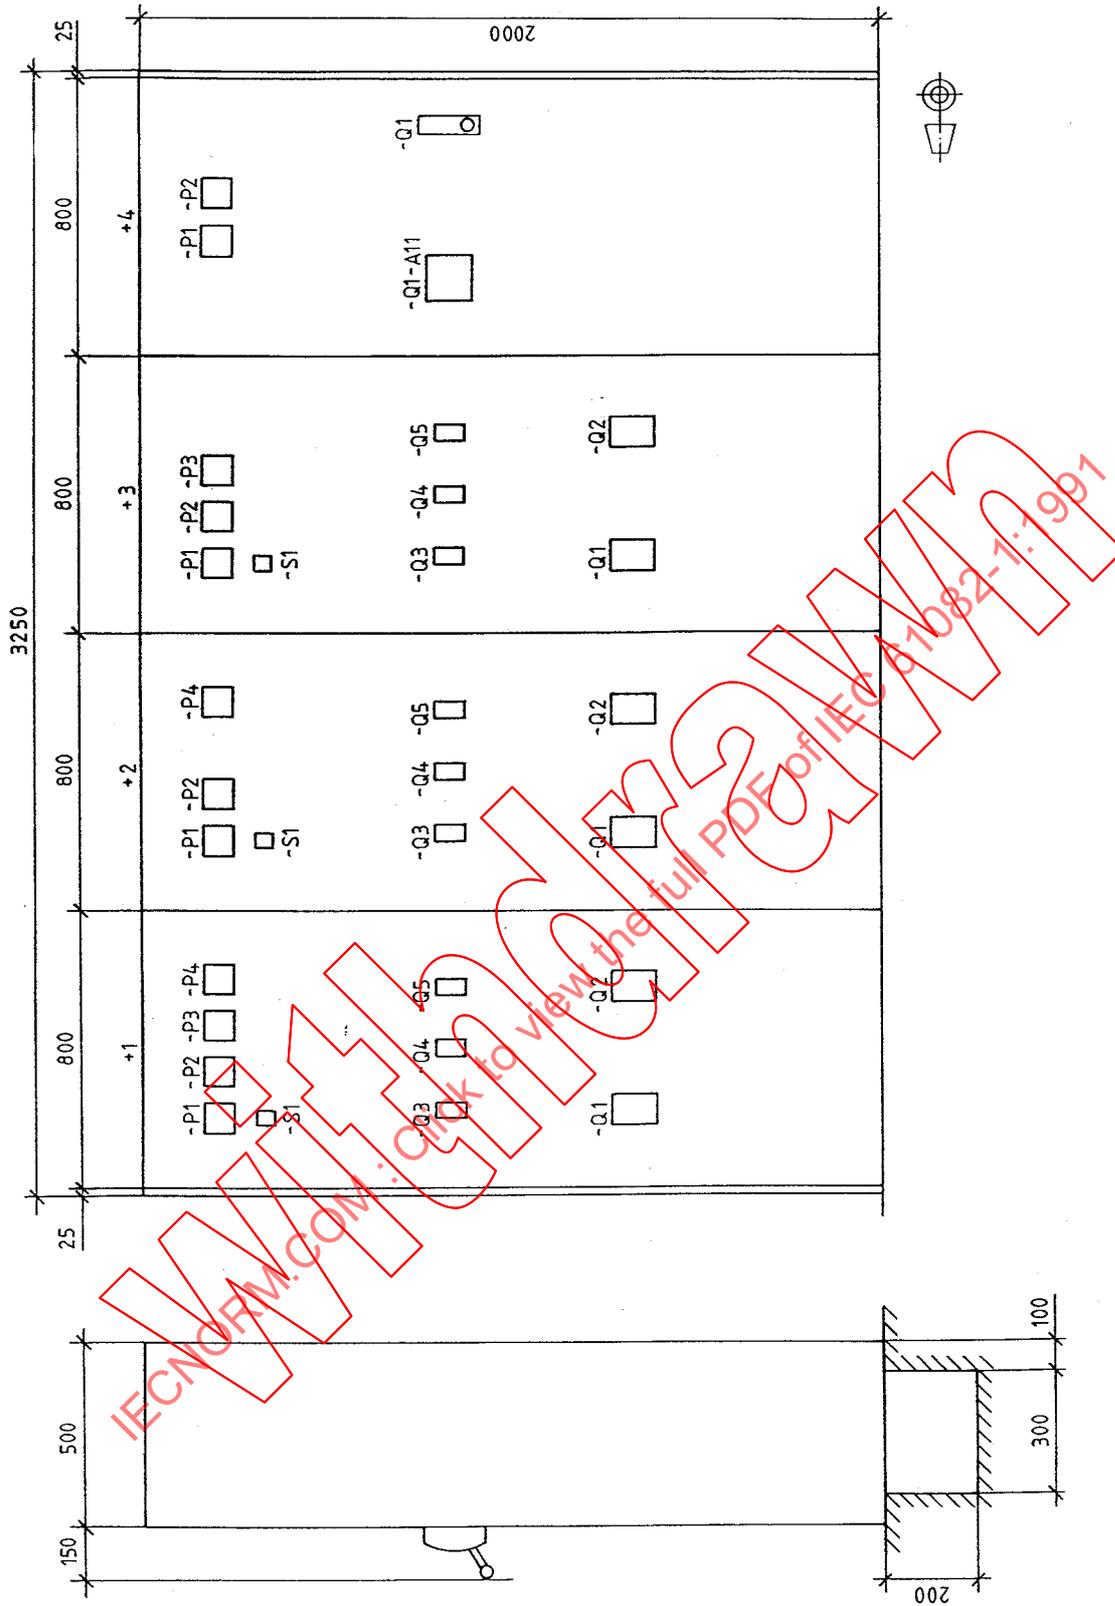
Exemple de dessin de disposition; ensemble d'appareillage +A sur la figure 25.
